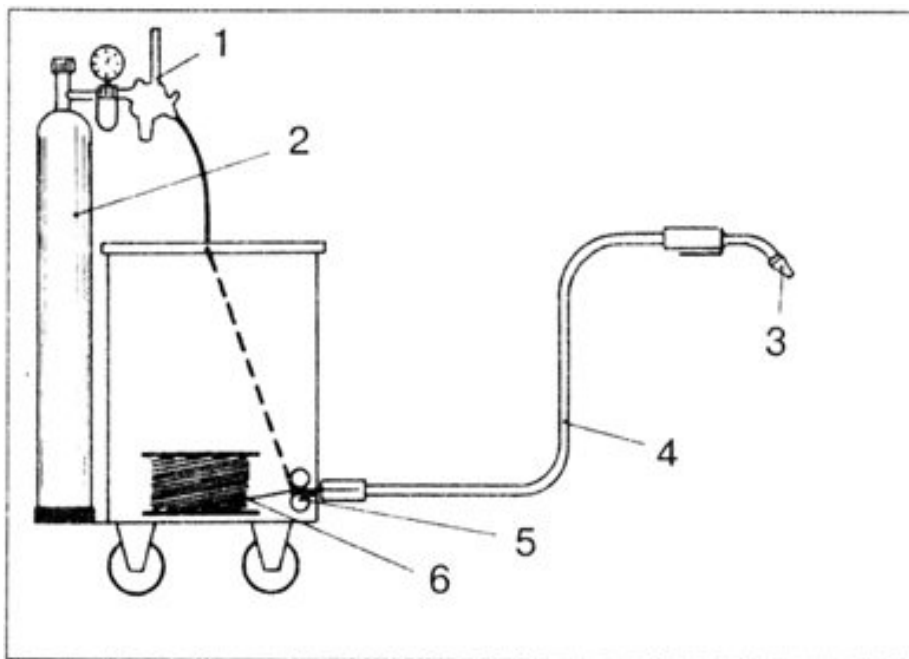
Схема аппарата для сварки в среде защитного газа:
